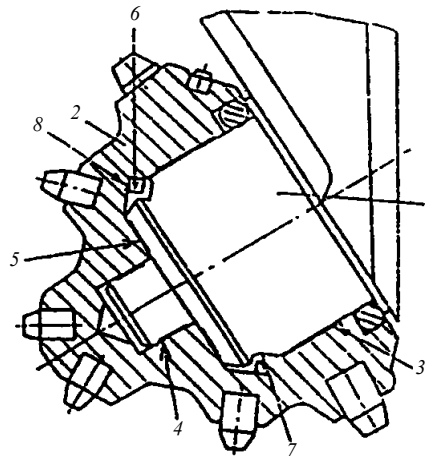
Конструкция опоры шарошечного долота (А. с. 1509504 А1 от 23.09.89): 1 – цапфа; 2 – шарошка; 3, 4 – подшипники скольжения радиальные; 4, 5 – упорные подшипники скольжения; 6 – стопорное кольцо (замковый узел); 7, 8 – посадочные канавки
